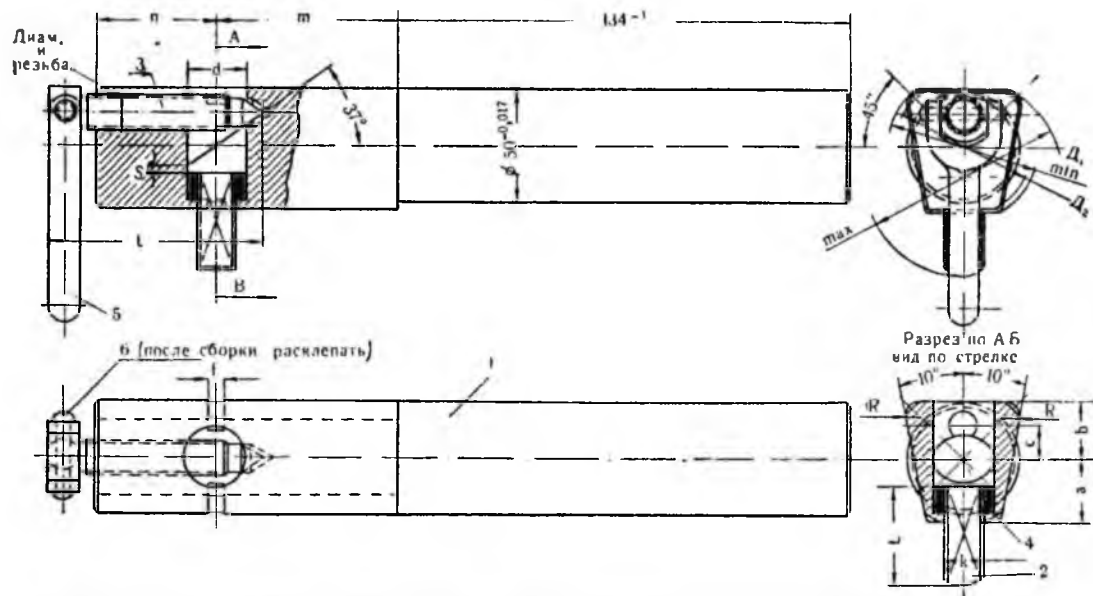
Универсальный палец для установки шатунов на плите прибора для проверки шатунов:
